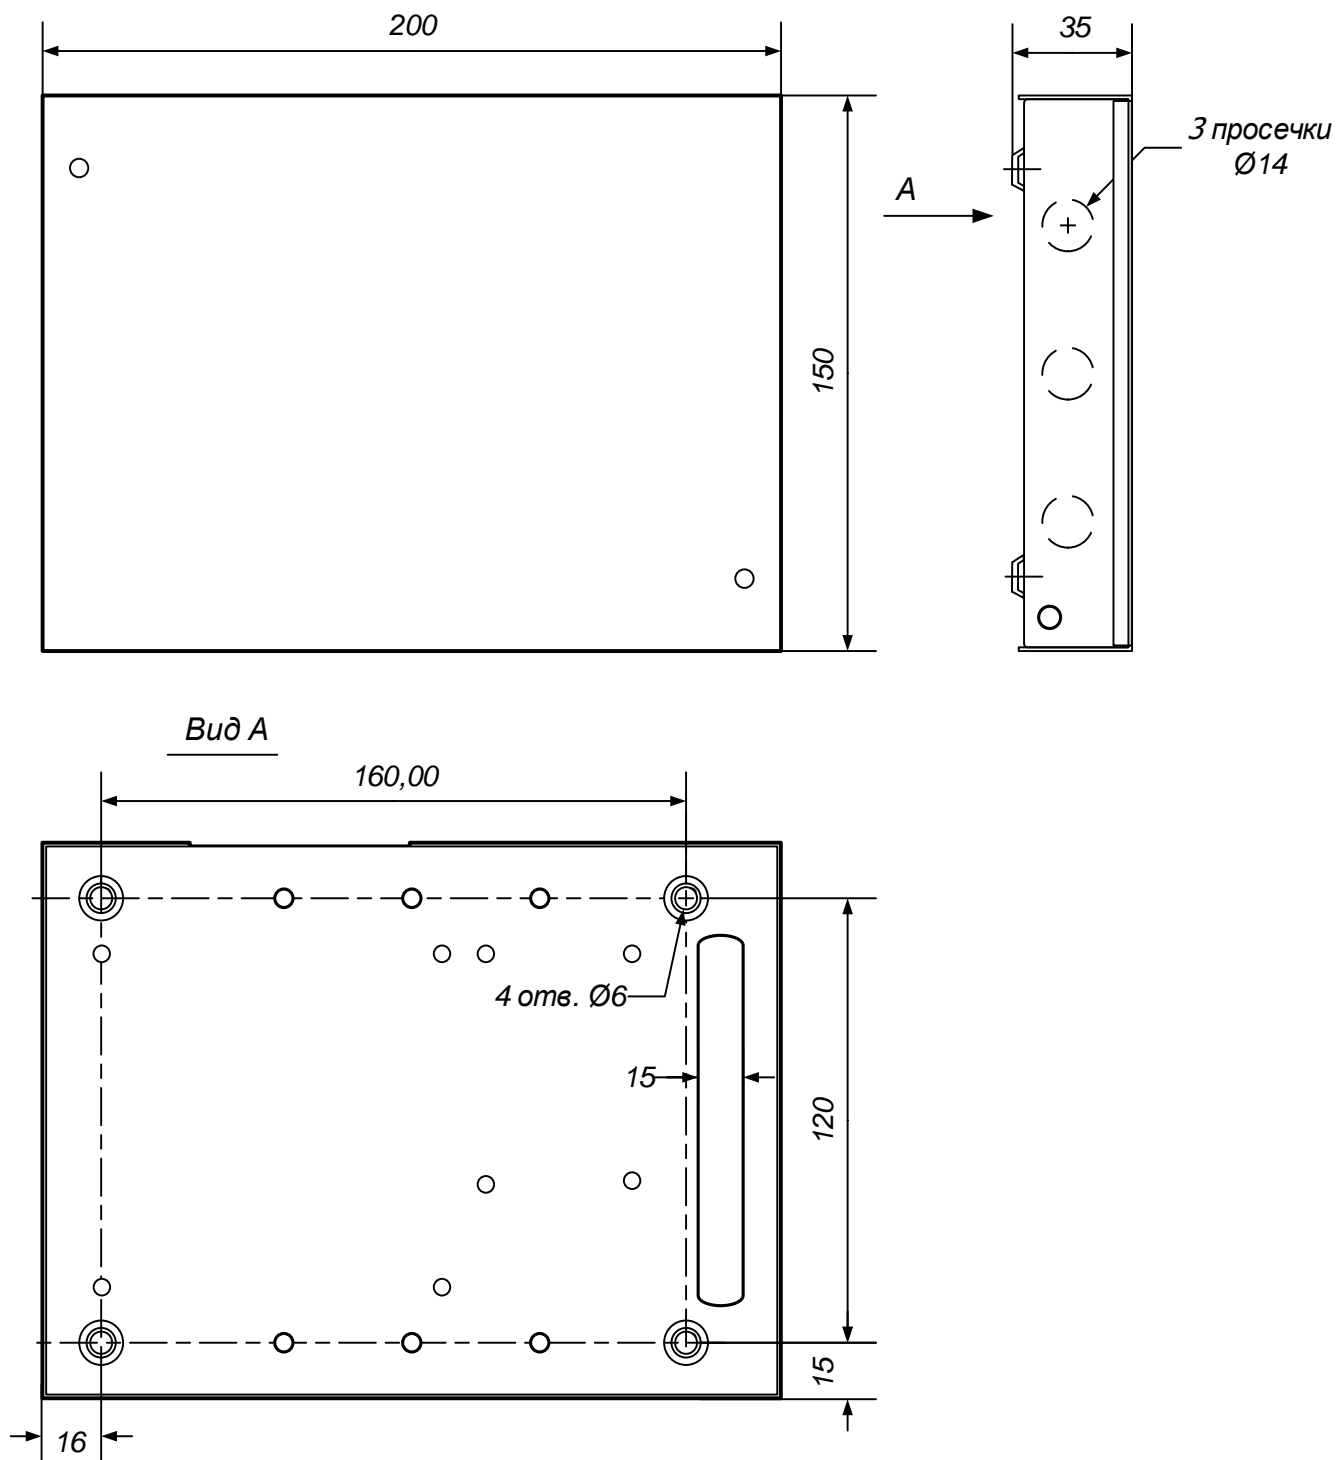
Габаритные и установочные размеры изделия в корпусе 075
